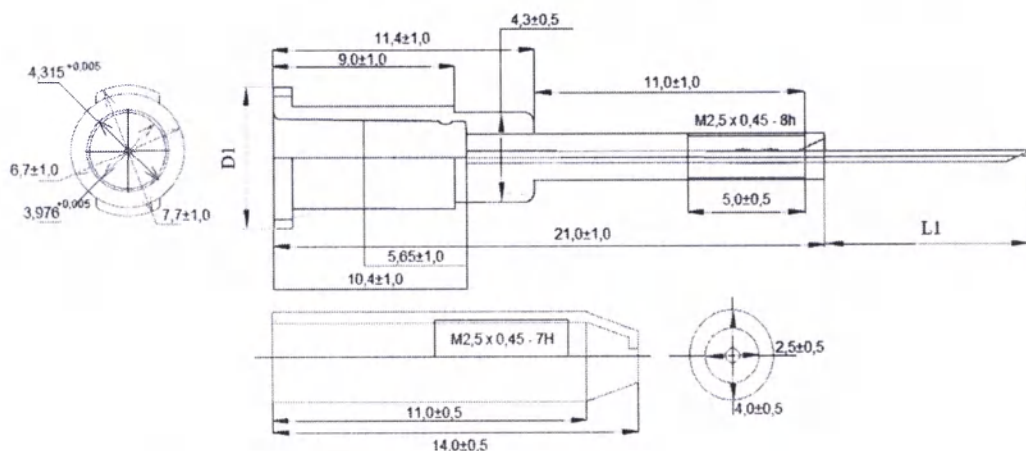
Размеры головки иглы Johns Screw Needle и «Луер» соединения по ISO 80369-7, присоединительный конус иглы по ISO 594-1
